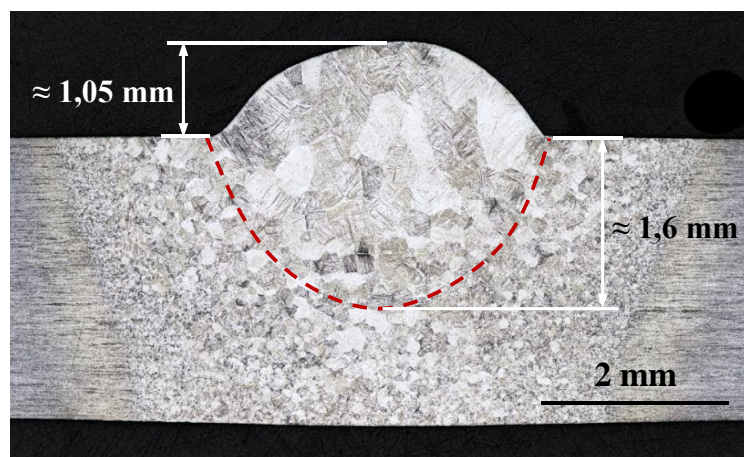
Auftragschweißung im Querschliff, ungeimpft; Grobkornzone eingefasst durch Strichlinie
